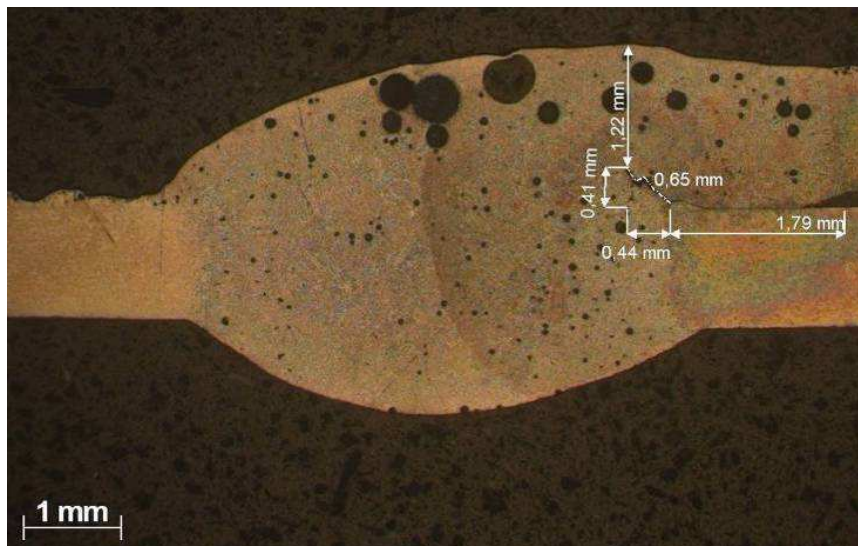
Schweißnahtquerschnitt von einem beöltem TAF Blech - C.s.84.1
